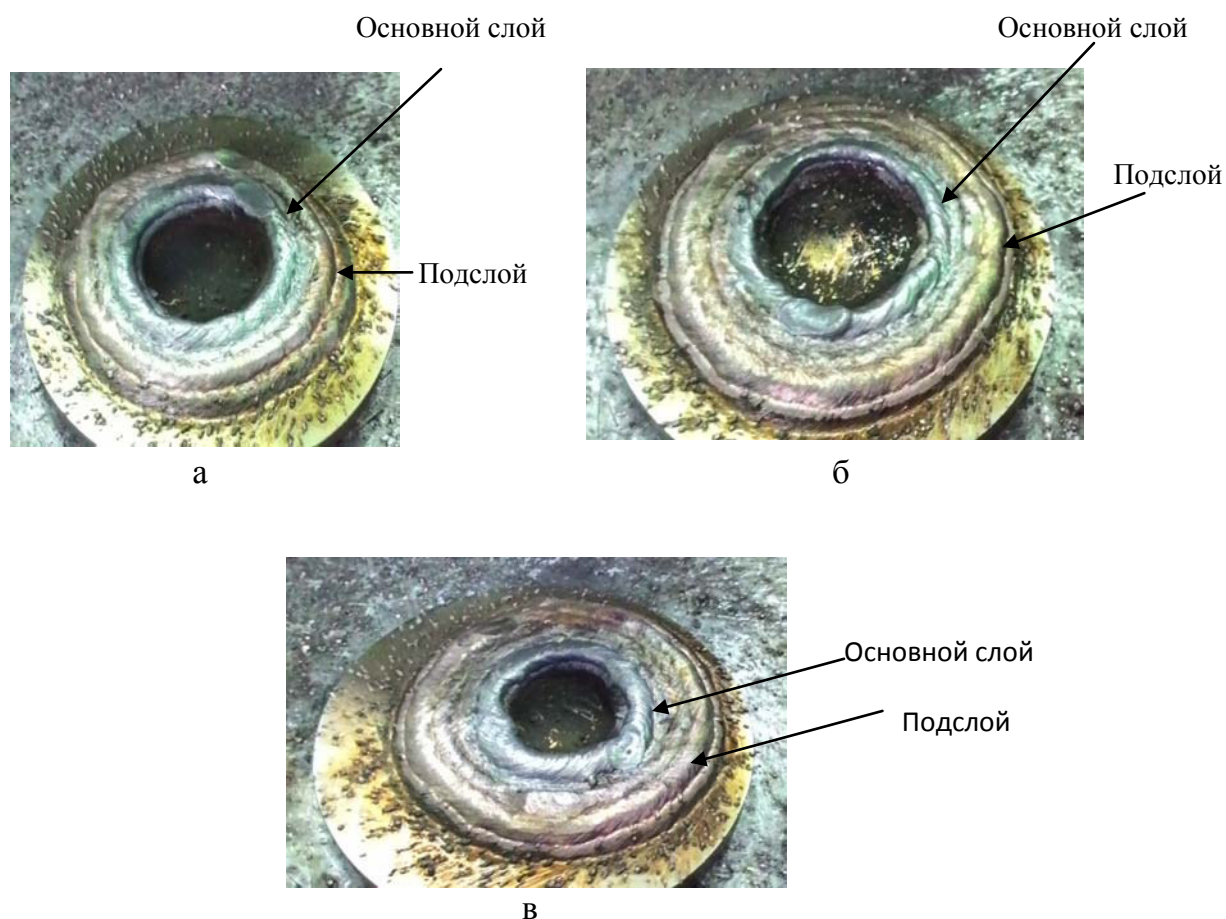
Внешний вид валиков металла основного слоя, наплавленного сварочной проволокой Св-МНЖМцТК40-1-10,3-0,1 на подслое на режимах:
